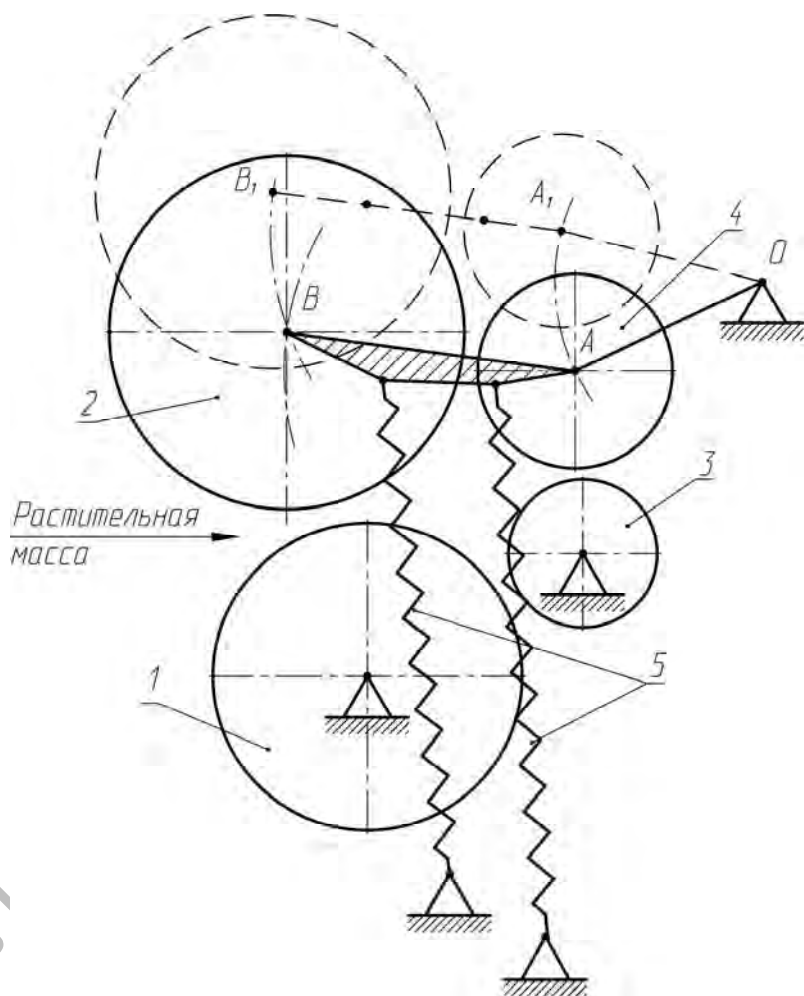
Схема механизма подпрессовки валцов питающего аппарата: 1, 3 – валцы нижние; 2, 4 – валцы верхние; 5 – пружины
